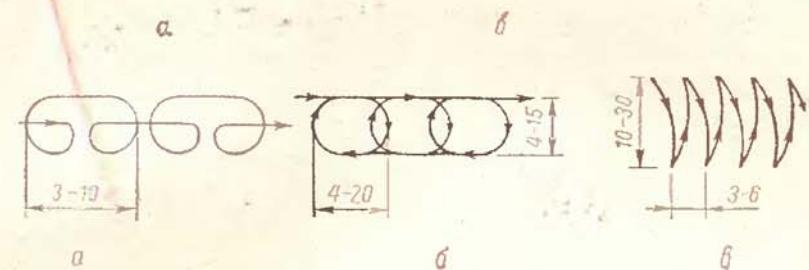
Схема перемещения электрода при полуавтоматической сварке в углекислом газе многослойных стыковых швов:
